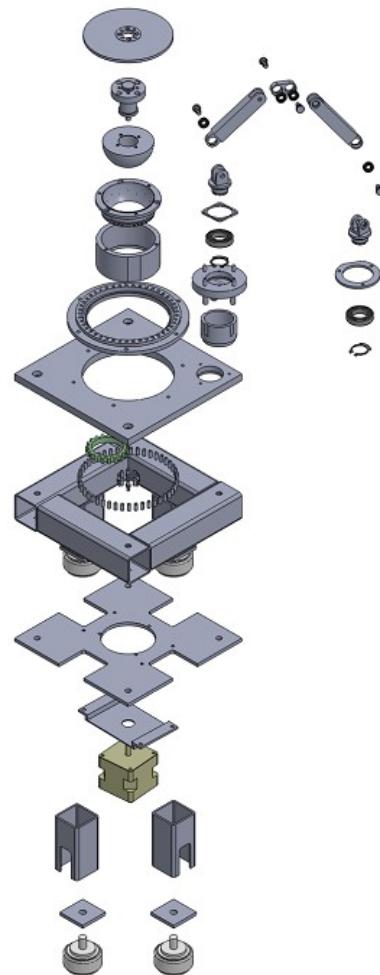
Desenho 3D da micro lapidadora explodida.
